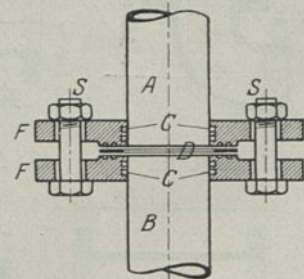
Rohrverbindung mit aufgelöteten oder aufgedrillten Flanschen.
